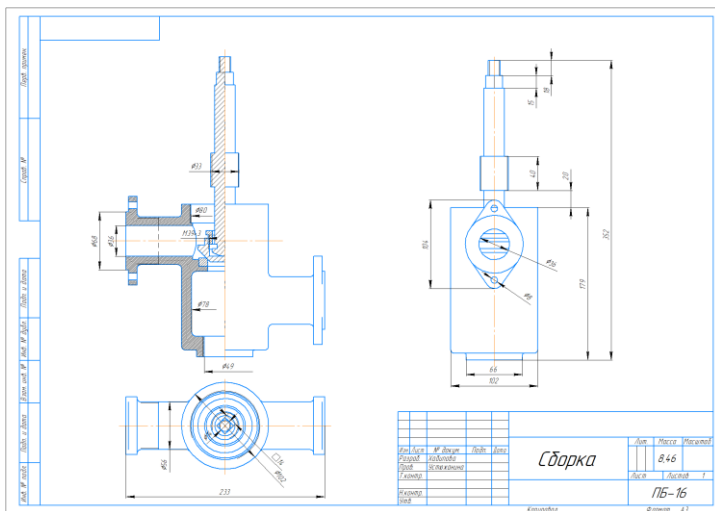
Сборочный чертеж фрагмента вентиля
